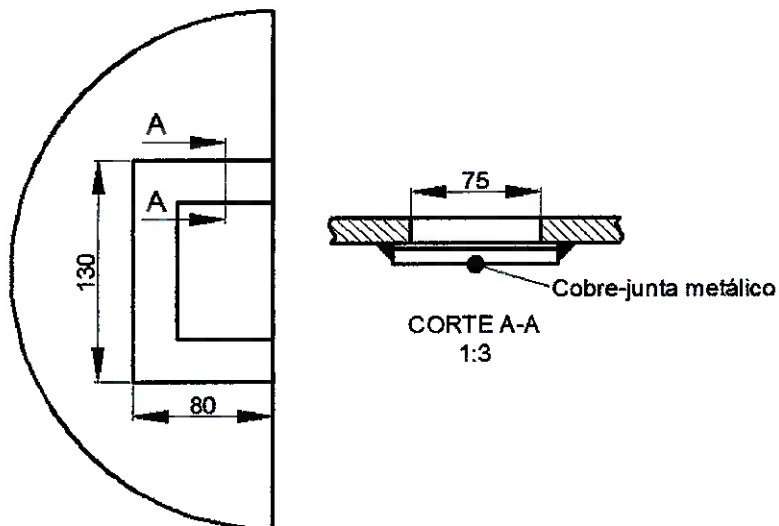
Dimensões dos chanfros preparados para soldagem
